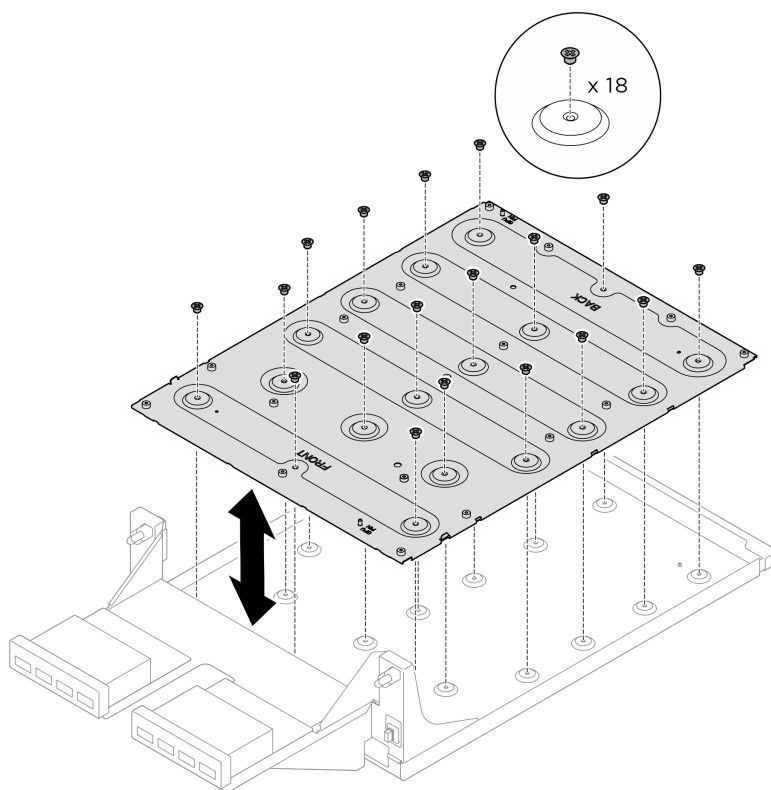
Extracción de la placa del adaptador del complejo de GPU
